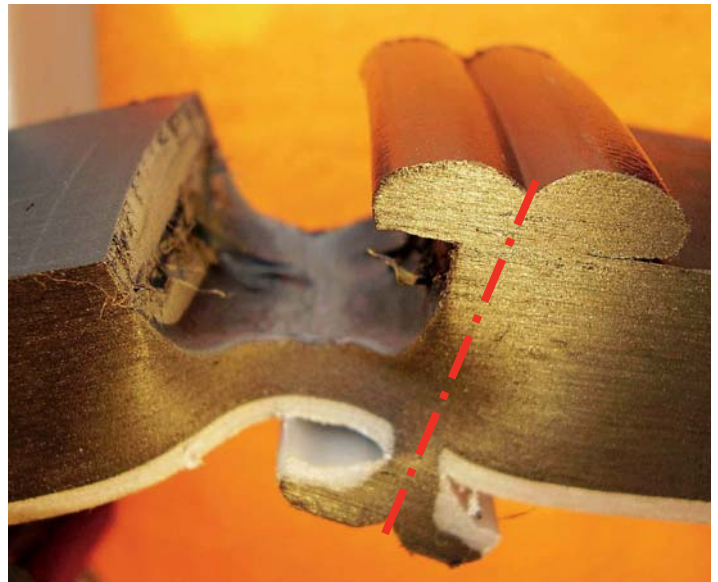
Bruchbild eines geschweißten Probekörpers, Bruchverlauf außerhalb der Fügeebene (rote Linie)
